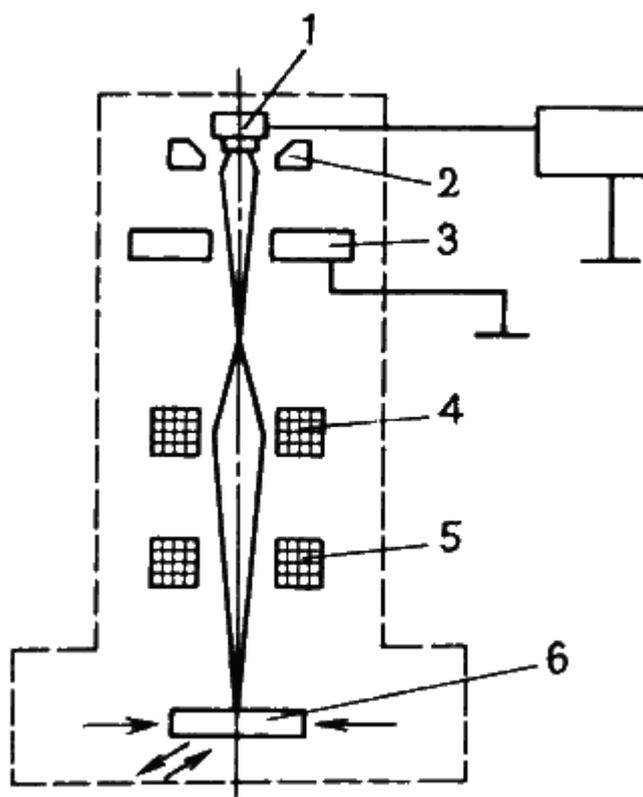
Схема установки для электронно-дуговой сварки
